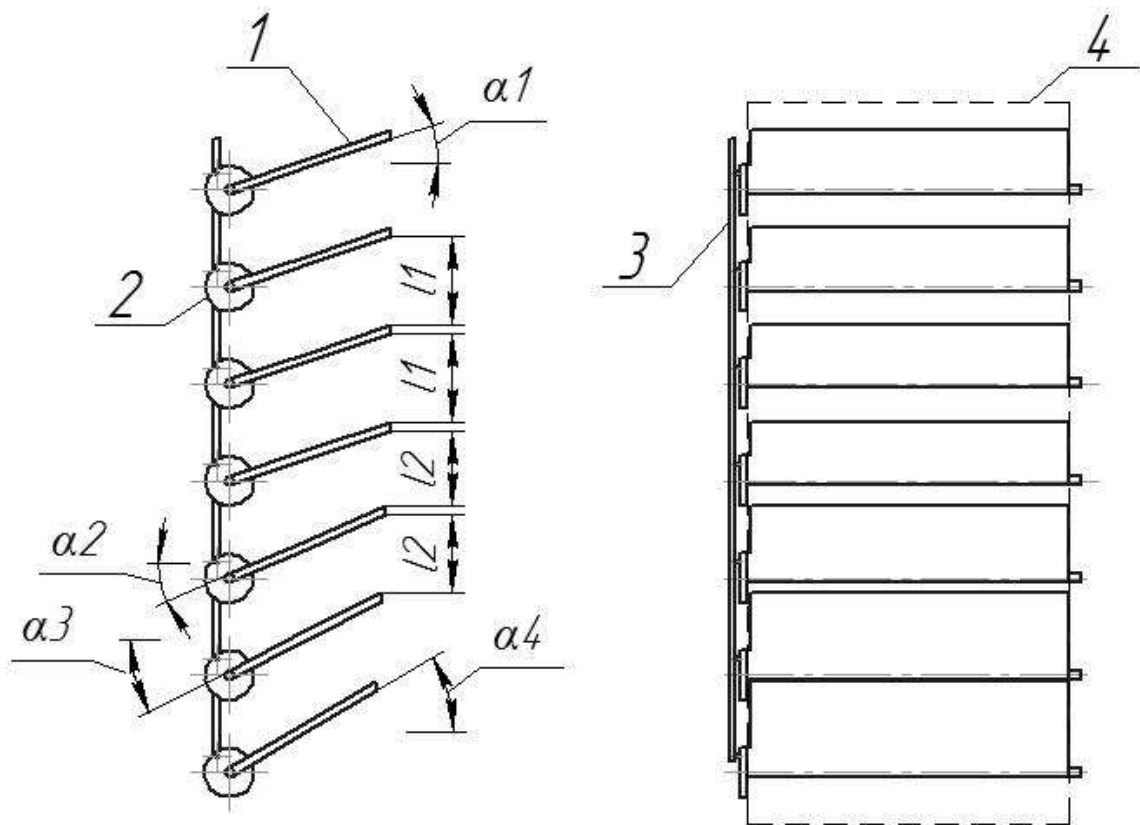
Схема удосконаленого струменевого генератора: 1 – пластина напрямна; 2 – вісь пластини; 3 – регулювальний пристрій; 4 – стінка корпусу
